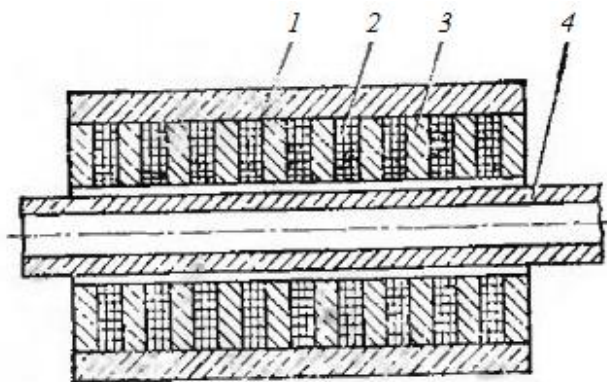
Трубчатый (коаксиальный) линейный двигатель:
